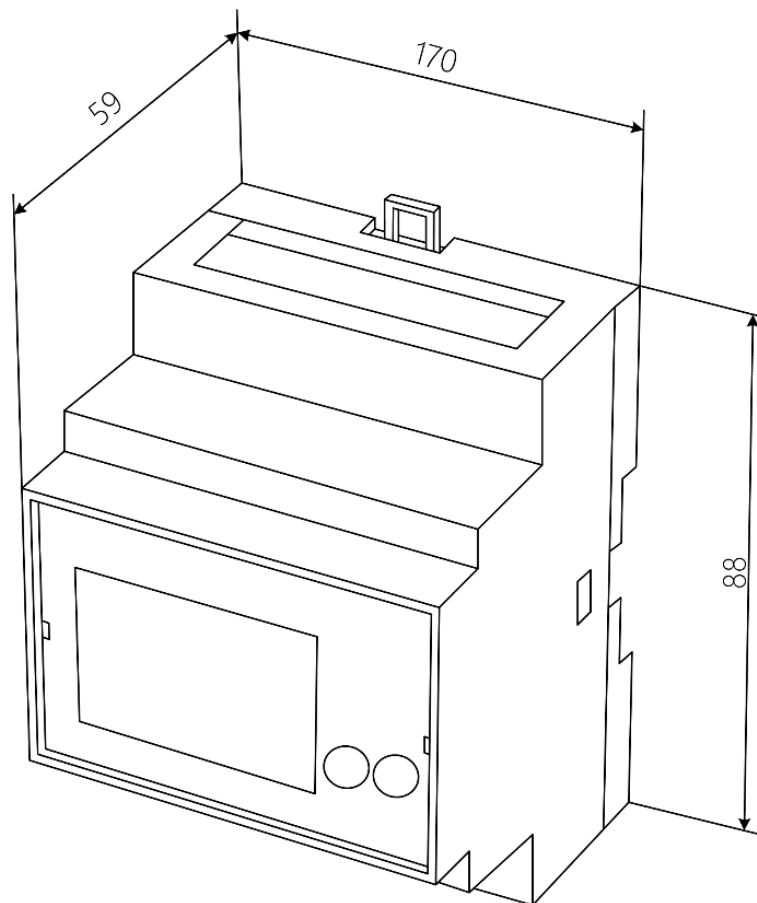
Габаритные размеры ПЛК «ВЭСТ-04»
